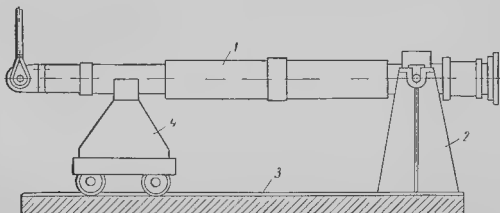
Приспособление для подъема ротора в вертикальном положении
